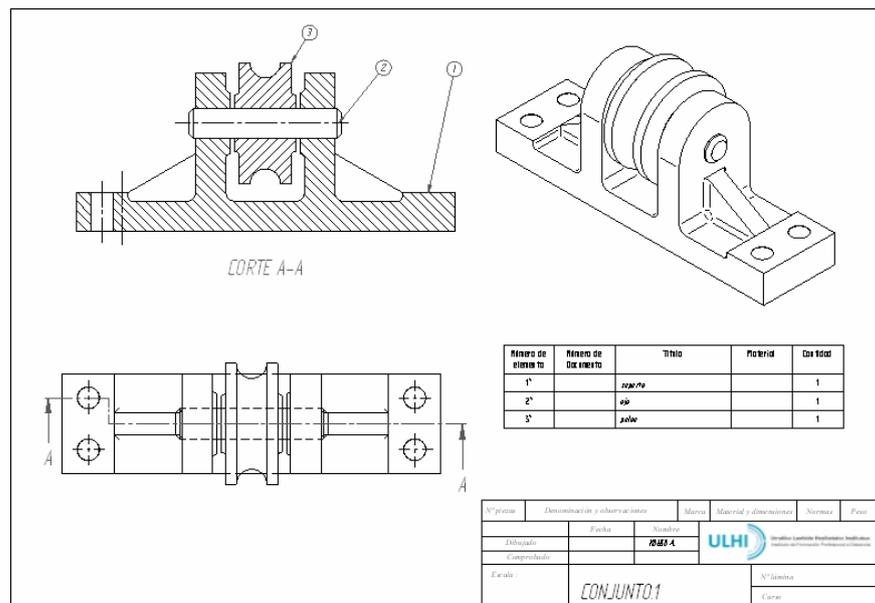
Ejemplo de un plano de conjunto (Fuente: Ikastaroak, 2020).
